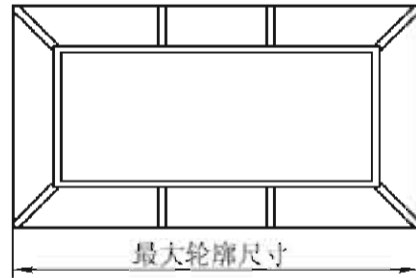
最终机械加工后铸件的最大轮廓尺寸
